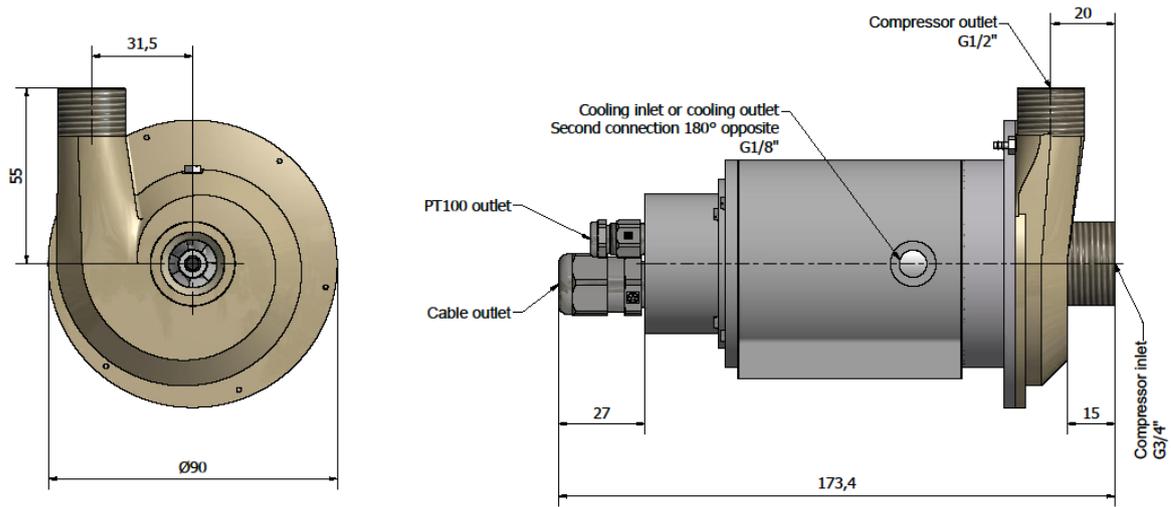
CAD Visualisierung des ausgelegten Luftlager-Turbokompressor-Prototypen.
